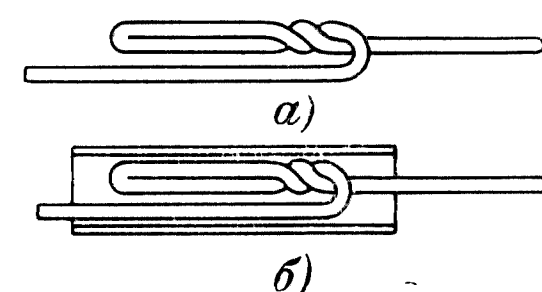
Сварка торцевой поверхности скрутки.
